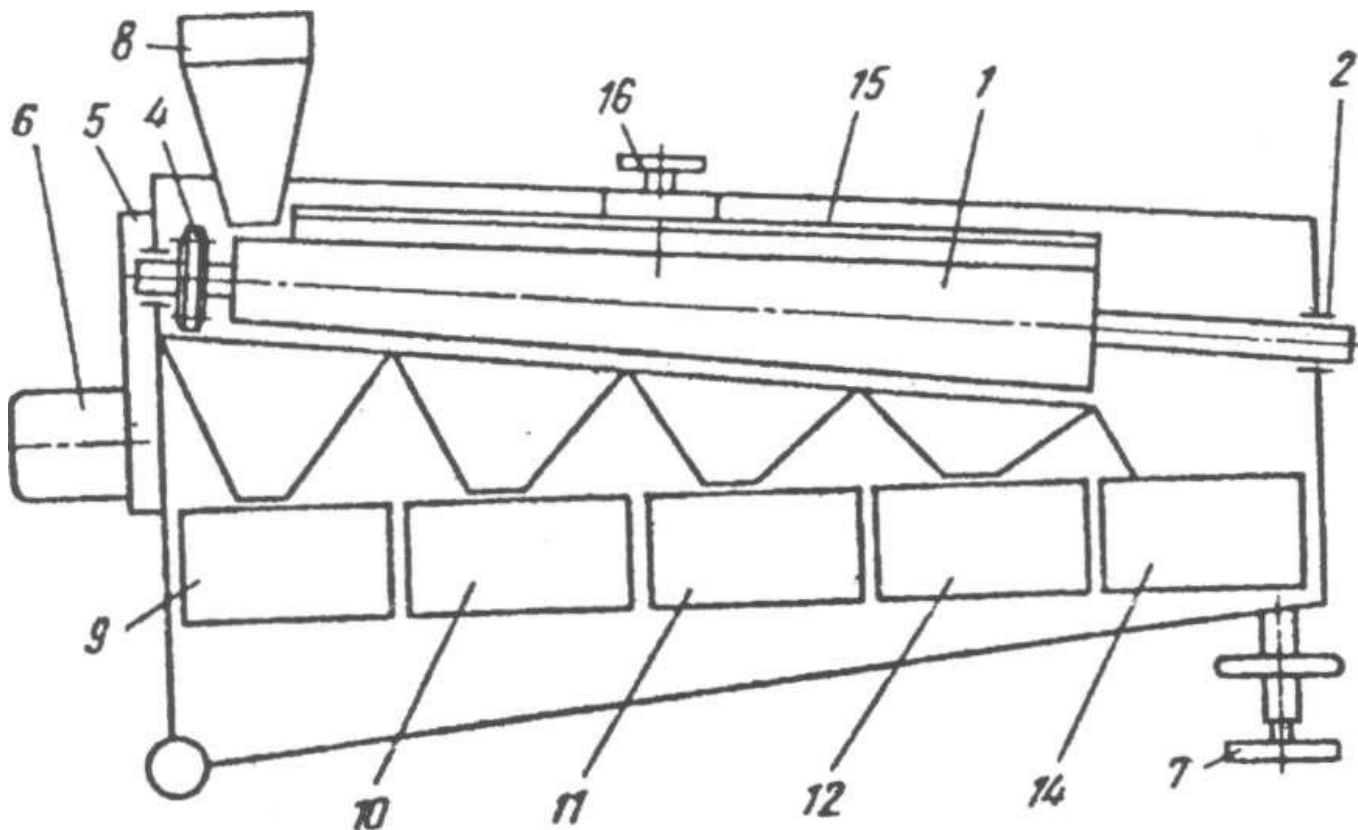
Конструктивна схема фрикційного сепаратора
